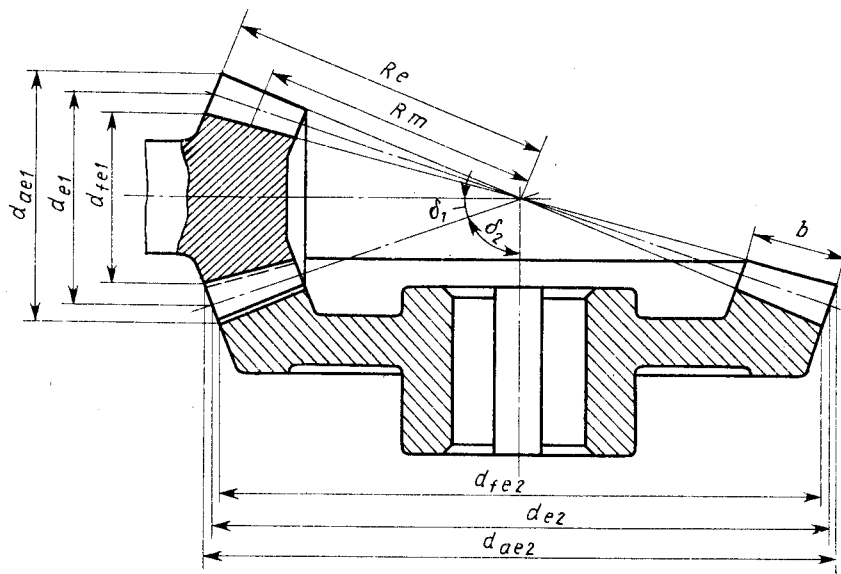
Геометрические параметры конической зубчатой передачи
